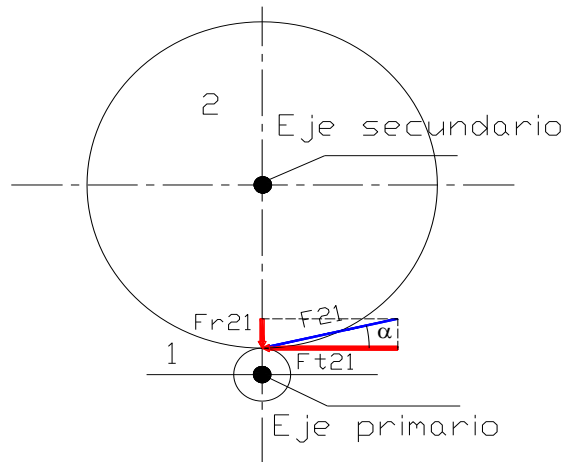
Esquema de fuerzas que actúan en los engranajes.
